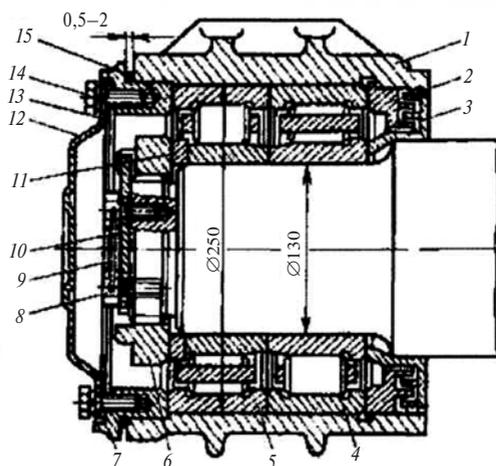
Букса грузового вагона с торцевым креплением цилиндрических роликовых подшипников корончатой гайкой М110:
